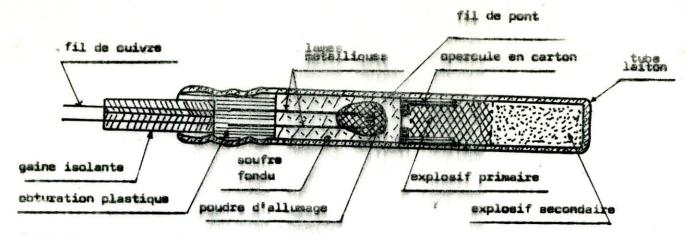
5CHEMA D'UN DETONATEUR ELECTRIQUE INSTANTANE.
